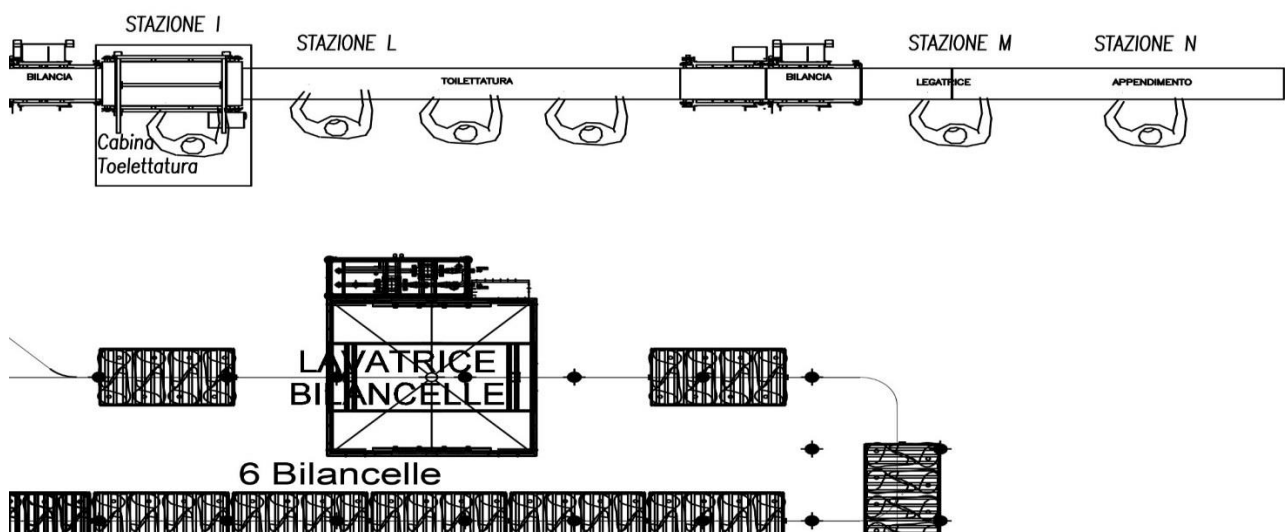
Layout parziale dell'impianto stazioni I+L+M+N
